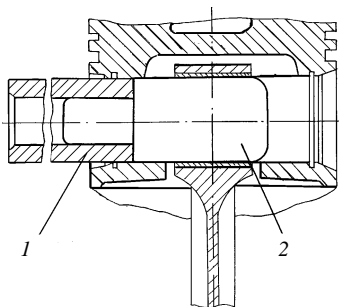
Сборка шатуна с поршнем и пальцем: 1 – палец; 2 – оправка
